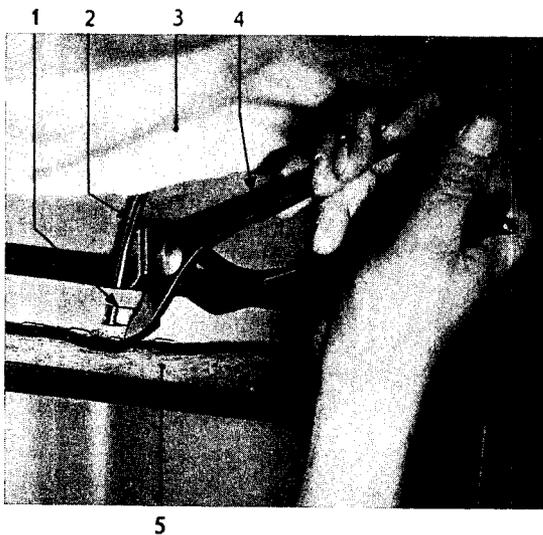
Spriegelhalterungen im Dachrahmen zusammendrücken
